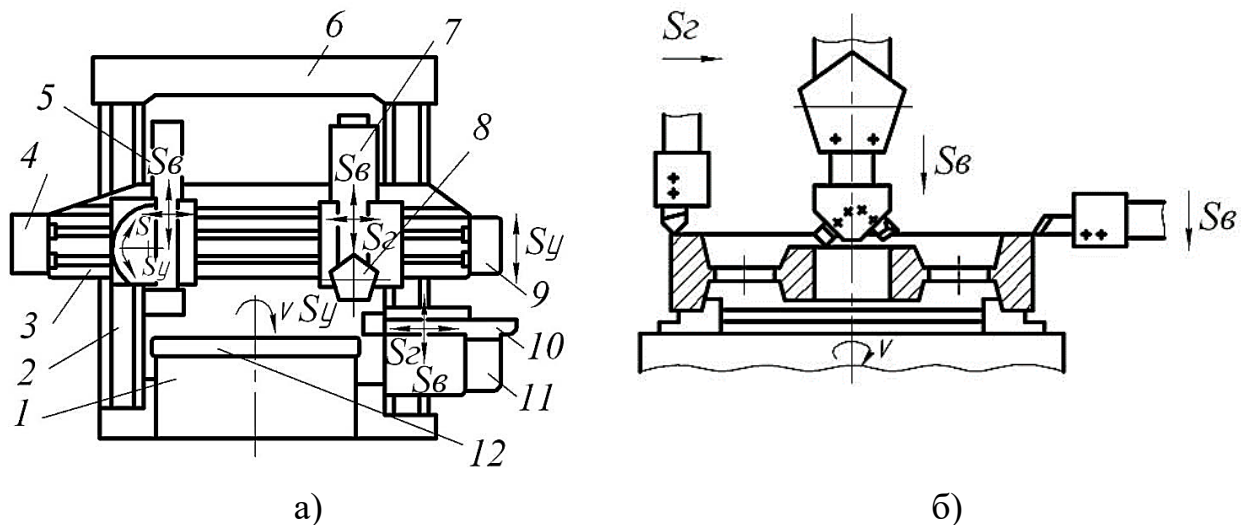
Схеми токарно-карусельного верстата (а) і обробки на ньому заготовки (б)
